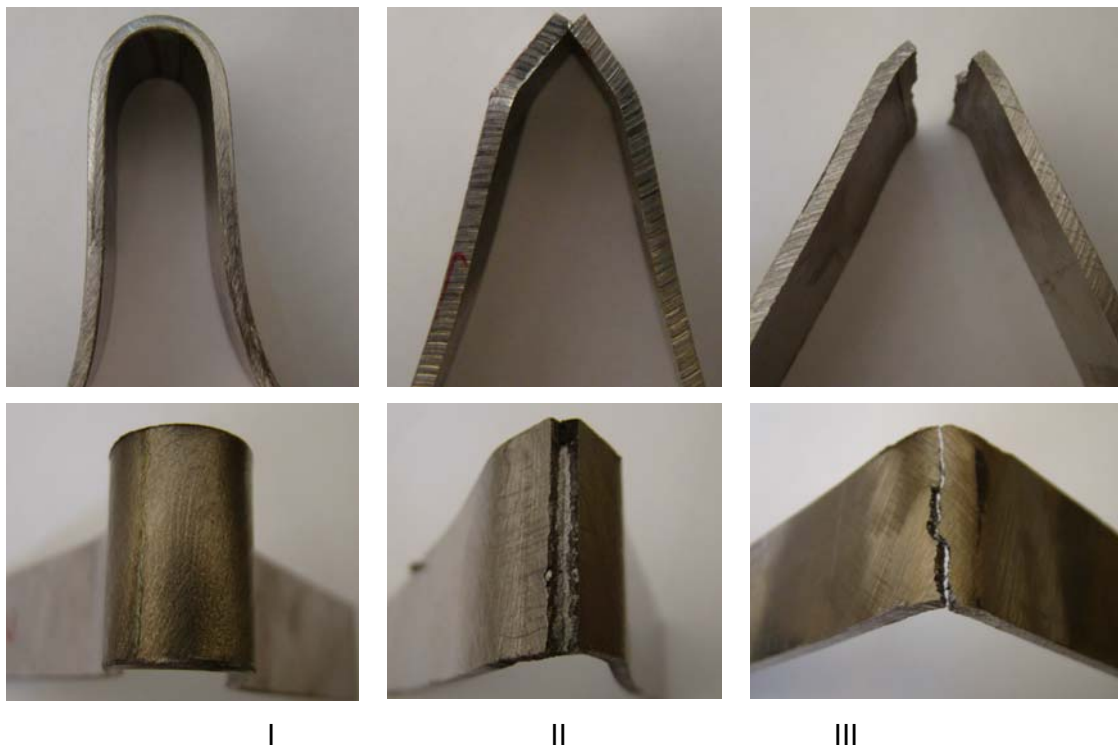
Corpo de prova onde (I) não ocorreu trinca ou rompimento no cordão de solda; (II) ocorreu rompimento devido à falha de soldagem (falta de fusão) no cordão de solda; (III) ocorreu rompimento devido à fragilidade do cordão de solda
